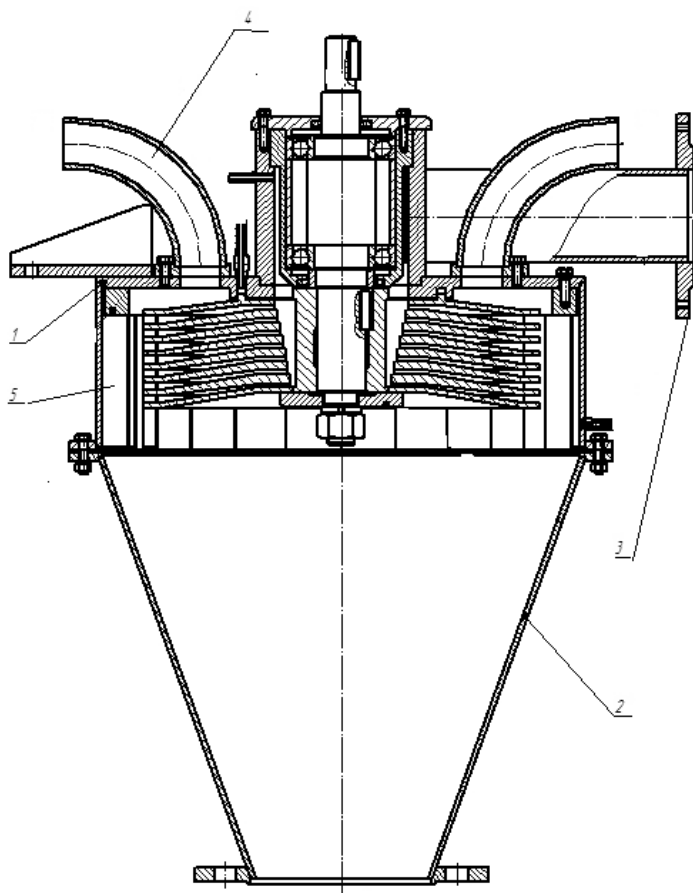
Воздушно-центробежный проходной классификатор конструкции кафедры МиАХП СПбТИ (ТУ): 1 – корпус; 2 – днище; 3 – патрубок выхода избыточного воздуха; 4 – патрубок выхода циркулирующего воздуха; 5 – жалюзи.
